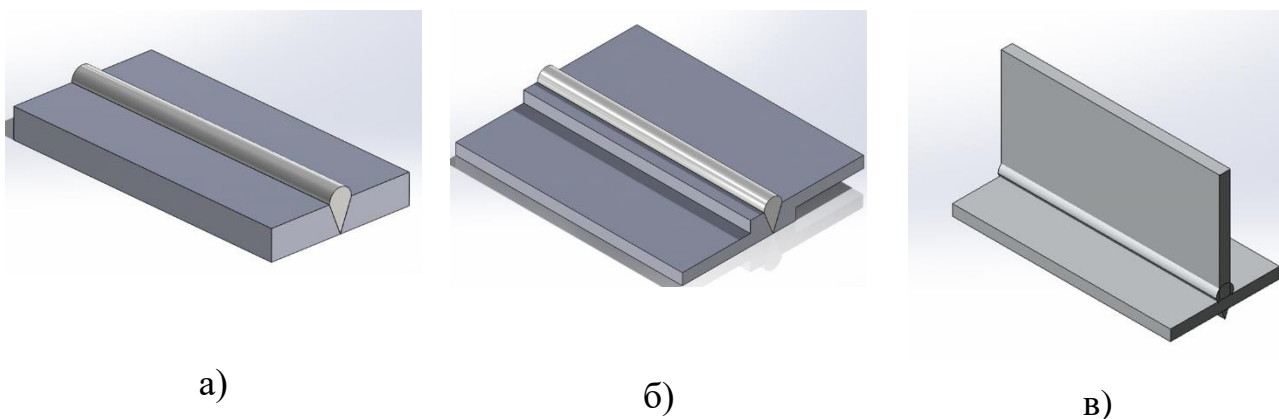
Типовые виды лазерных сварных соединений листового материала.
